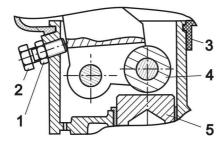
Регулировка тормозного крана 1-контргайка; 2-регулировочный болт; 3-оболочка; 4-ролик; 5-толкатель
